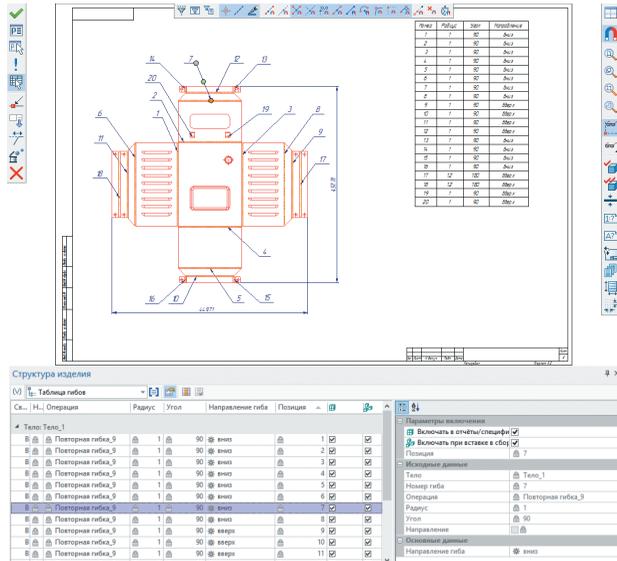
Развертка листовой детали с номерами гибов и таблицей гибов
